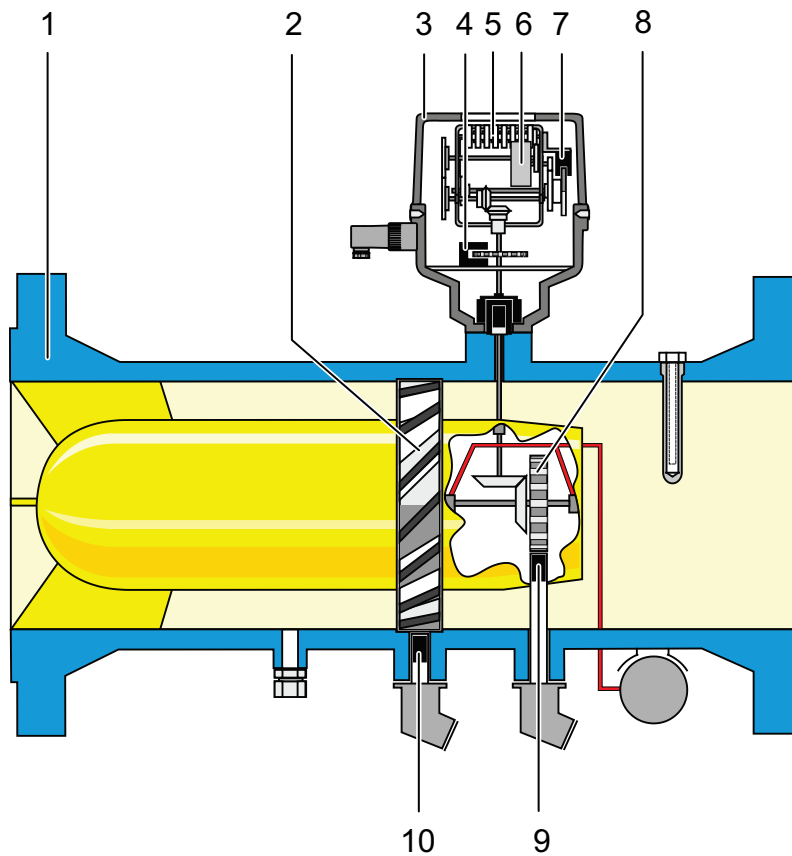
Schnittzeichnung Turbinenradgaszähler (exemplarisch)
